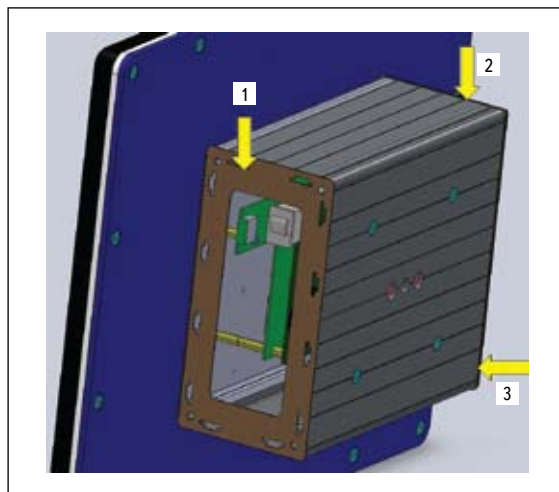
Обеспечение герметичности блока управления (корпус со снятой боковой крышкой)
